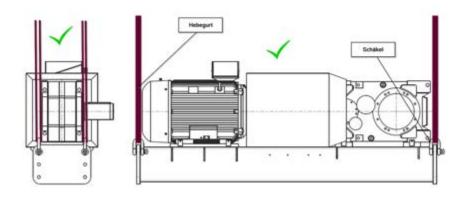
Транспортировка редуктора с механизмом для перемешивающих устройств
